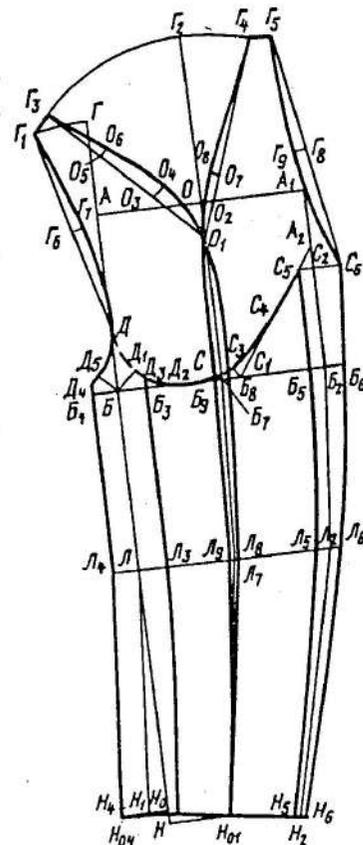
Чертеж рукава покроя реглан для легкой куртки
